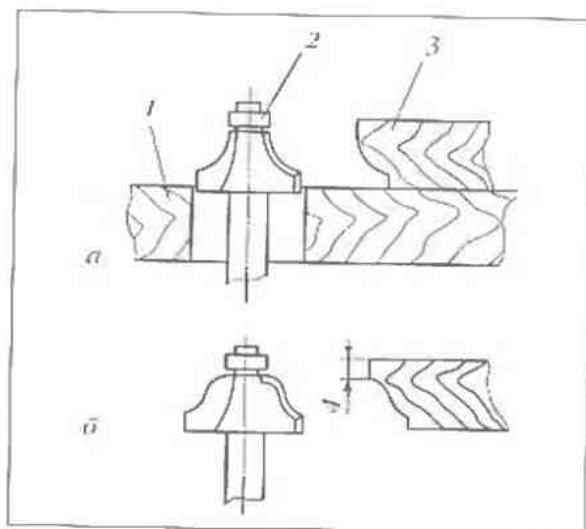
Фасонная обработка кромок: а – на фрезерном станке; б – фрезой оптимального профиля; 1 – рабочий стол; 2 – подшипник-ограничитель фрезы; 3 – обрабатываемая деталь
